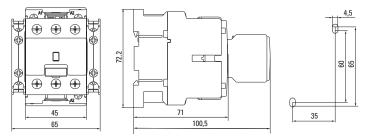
Габаритные и установочные размеры контакторов КМЭ 25А, КМЭ 30А
